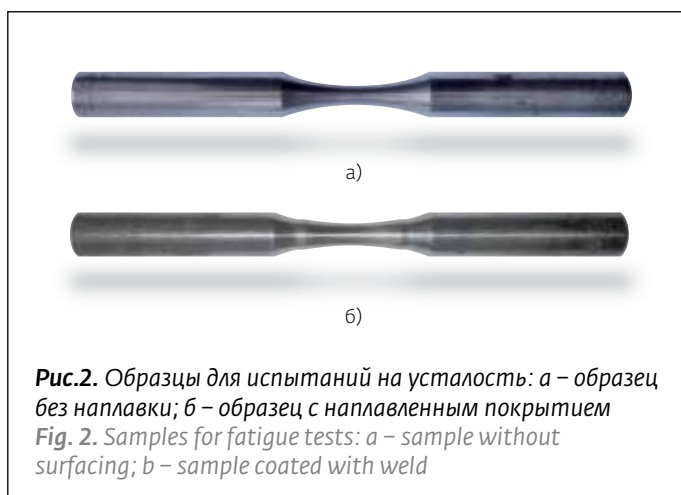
Образцы для испытаний на усталость: а – образец без наплавки; б – образец с наплавленным покрытием
